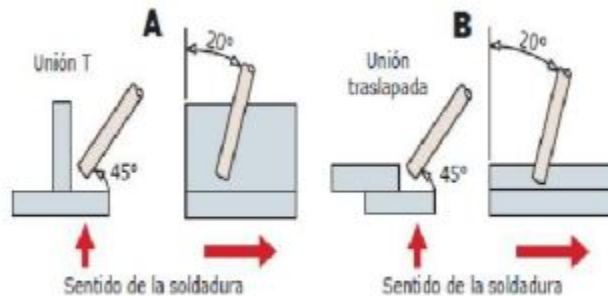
Ángulos de los electrodos para soldadura de filete
